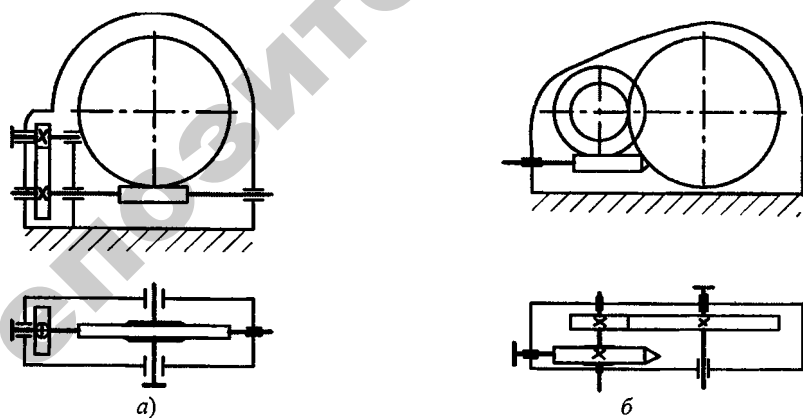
Схемы: а – зубчато-червячного редуктора; б – червячно-зубчатого
